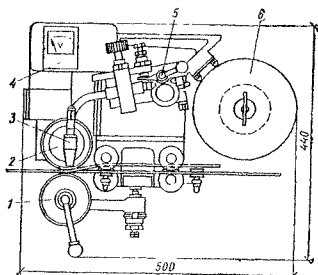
Сварочный трактор ТС-49 для автоматической сварки тонколистовой стали на катящейся подкладке в среде углекислого газа
